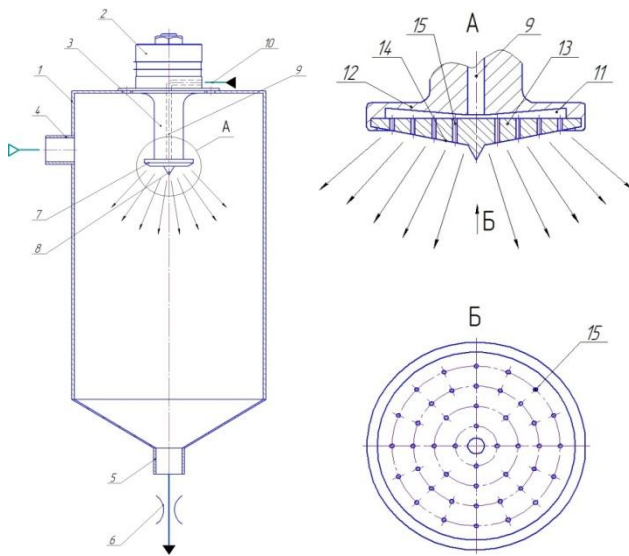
Схема пристрою для обробки рідини (1 – камера розпилю; 2 – перетворювачі; 3 – трансформатор коливальної швидкості; 4 – патрубок для підводу рідини; 5 – патрубок для відводу рідини; 6 – дросель; 7 – грибовидна частина; 8 – конусний гострокінцевий елемент; 9 – центральний канал; 10 – трубопровід; 11 – центральна частина щілинної порожнини; 12 і 13 – дві акустично контактуючі та механічно з'єднані частини; 14 – поверхня розпилення; 15 – отвори)
